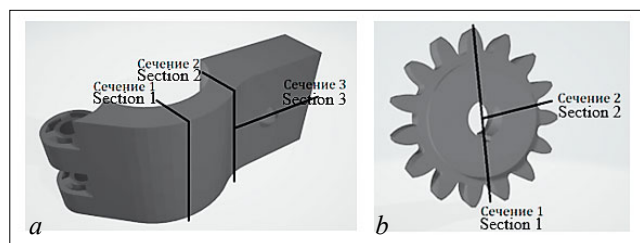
Схема резки опоры пальца (a) и шестерни (b)
